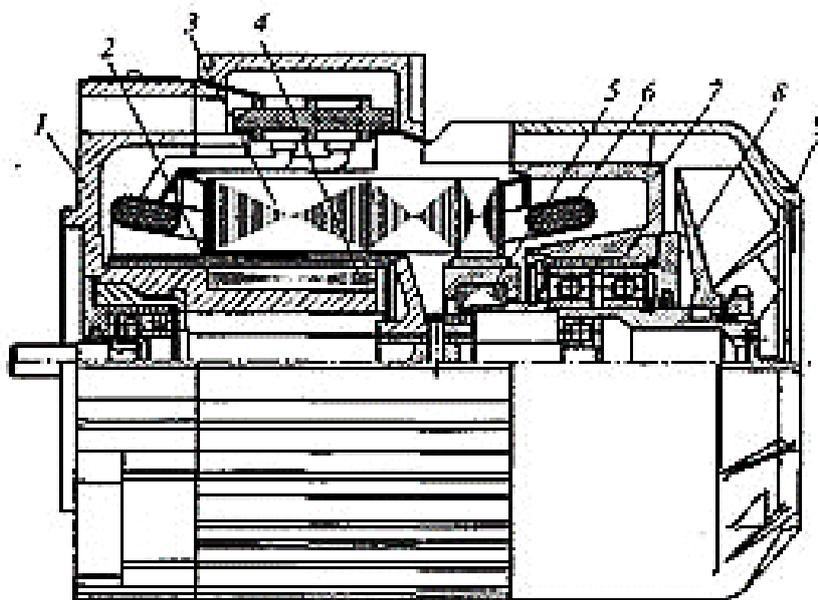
Асинхронный исполнительный двигатель типа ДАУ-63П
